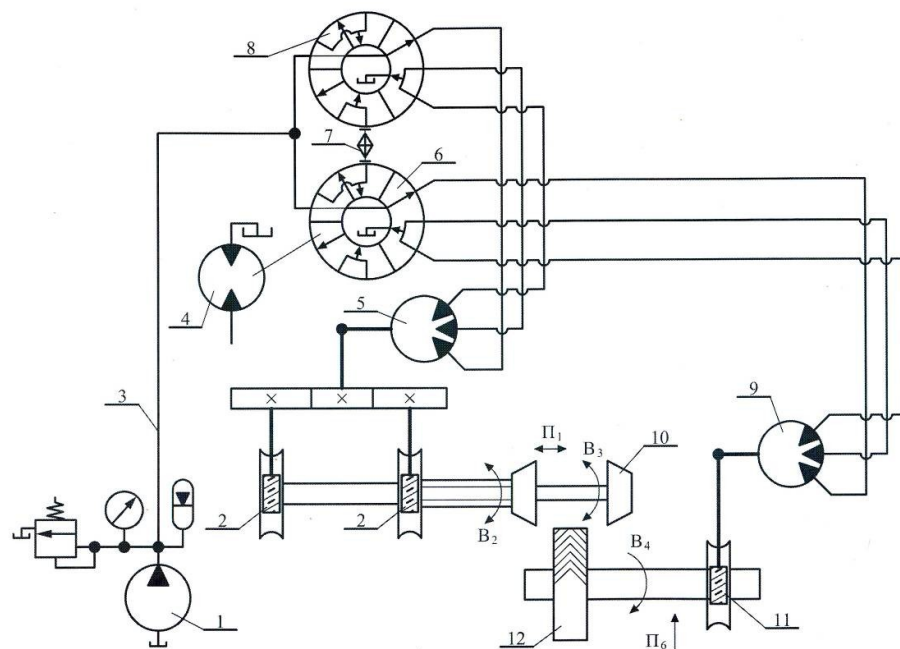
Схема гидравлической цепи деления (обката) зубодолбежного станка для нарезания шевронных зубчатых колес
